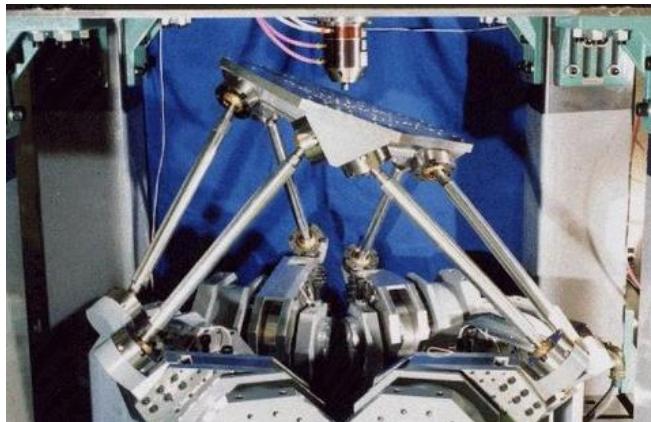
Шести координатный поворотный стол по схеме «ротопод»
